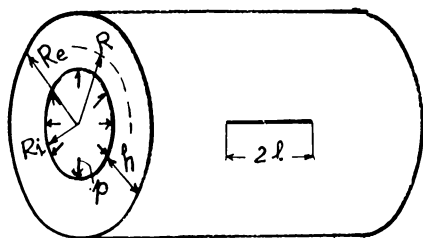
Conductă cu fisură longitudinală străpunsă
